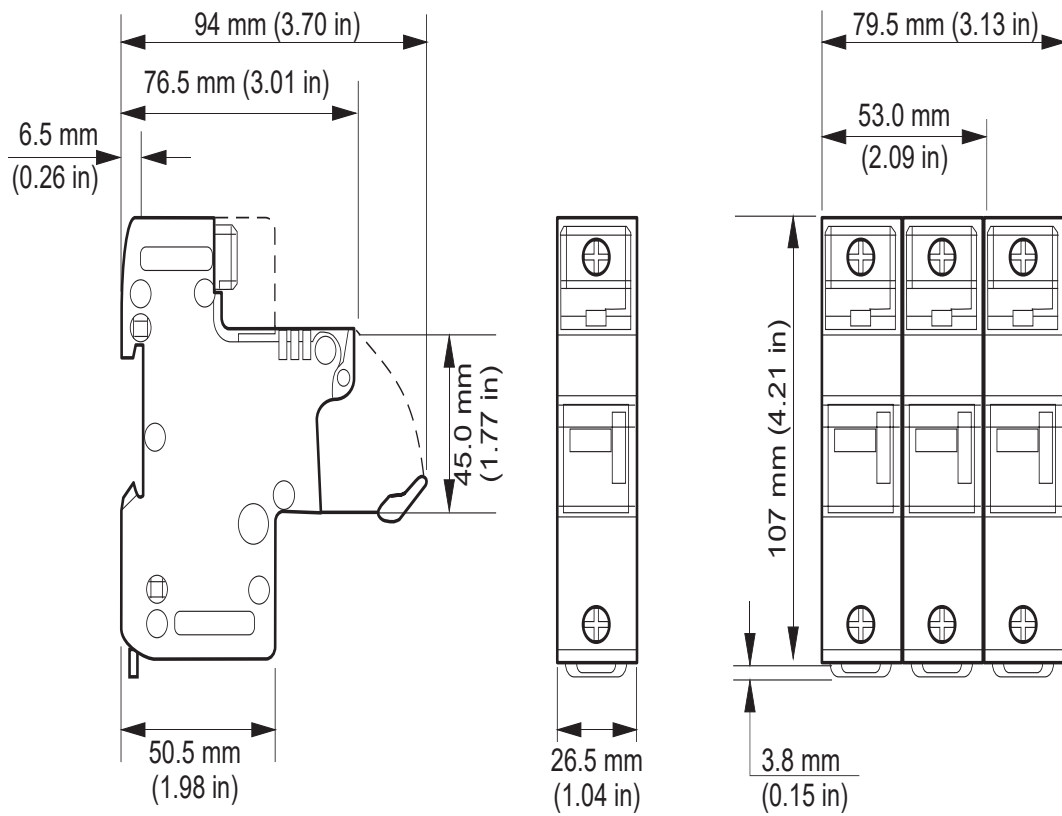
Las dimensiones del portafusibles: US141 (14x51 mm)
